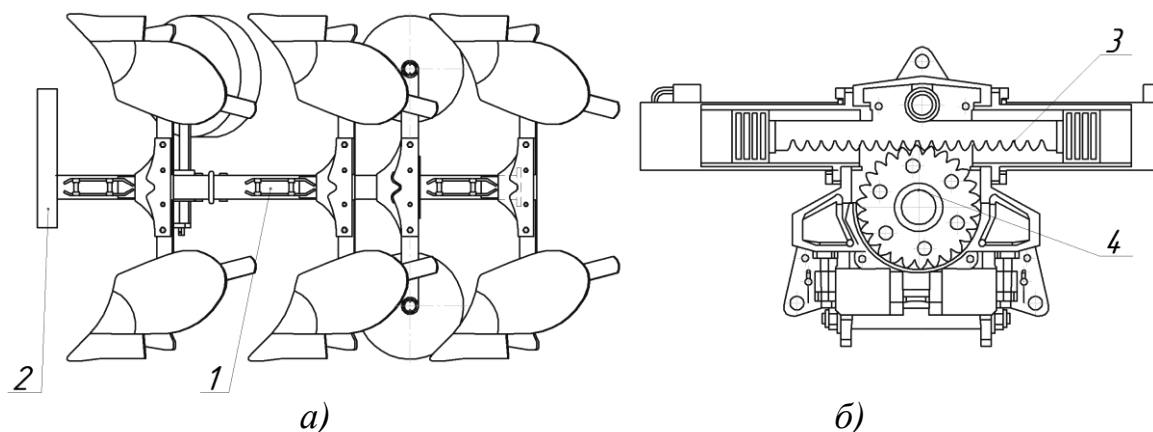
Плуг оборотный навесной: а) общая схема; б) схема оборотного механизма
